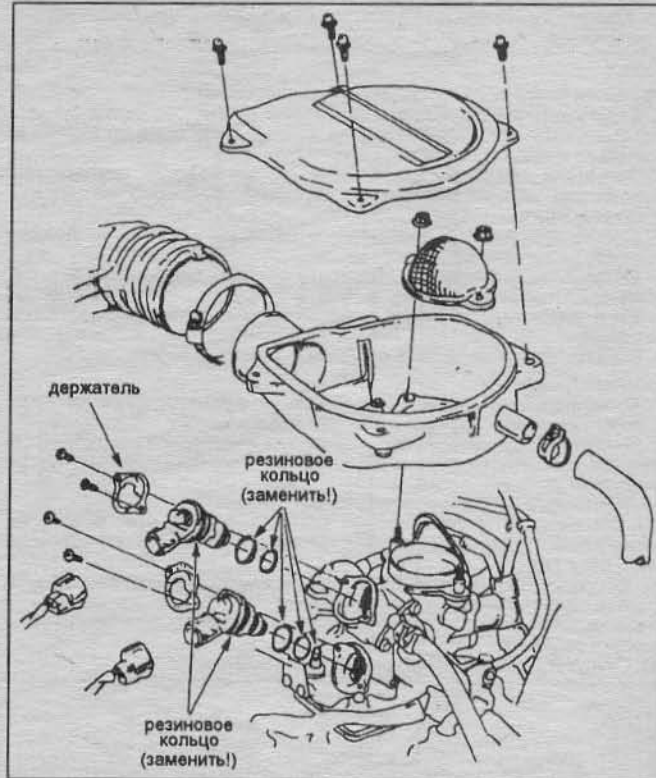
Установка форсунок (схема двухточечного впрыска).
